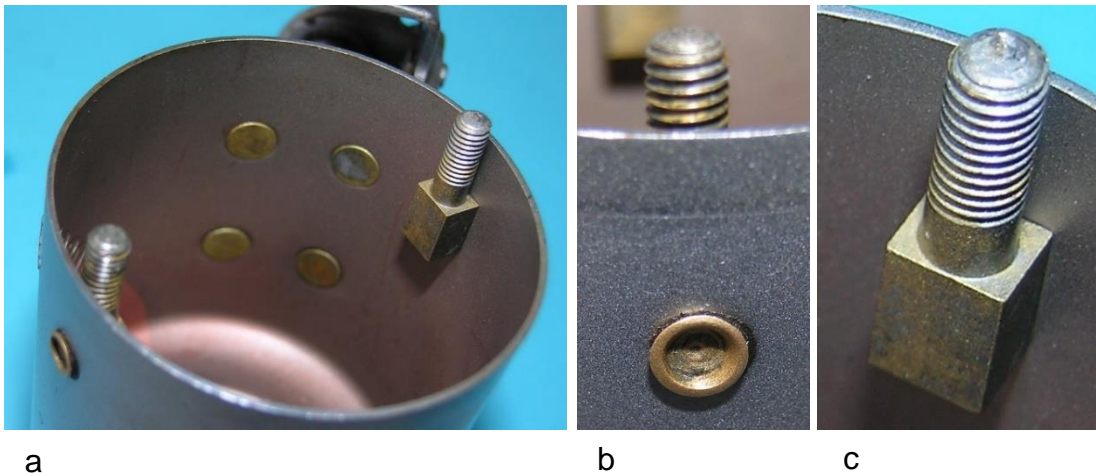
Gewindebolzen am Gehäusetopf: a) Flache Nietköpfe für den Flansch der Kippvorrichtung, b) Hohlriet zur Befestigung des Gewindebolzens, c) Angenieteter Gewindebolzen
